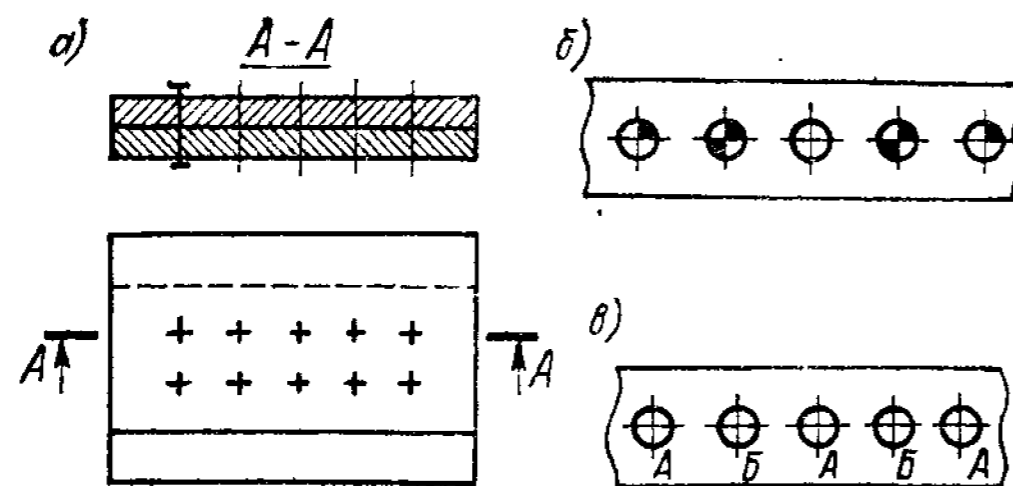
Условные изображения клепаных соединений: а — с заклепками одного типа и размера; б, в — с заклепками различных типов и размеров
